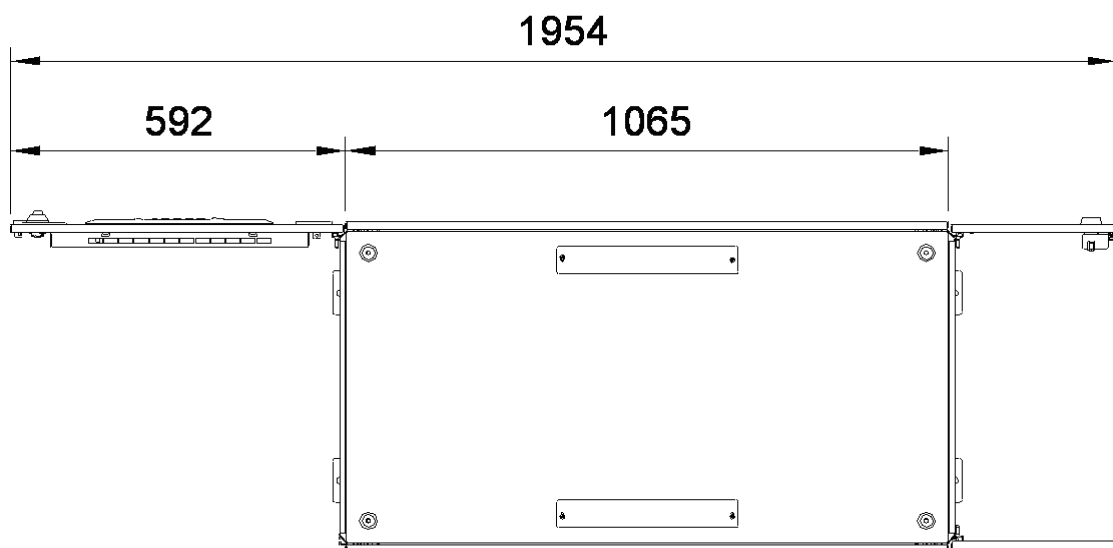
Вид ИБП и батарейного шкафа сверху с открытыми дверцами
